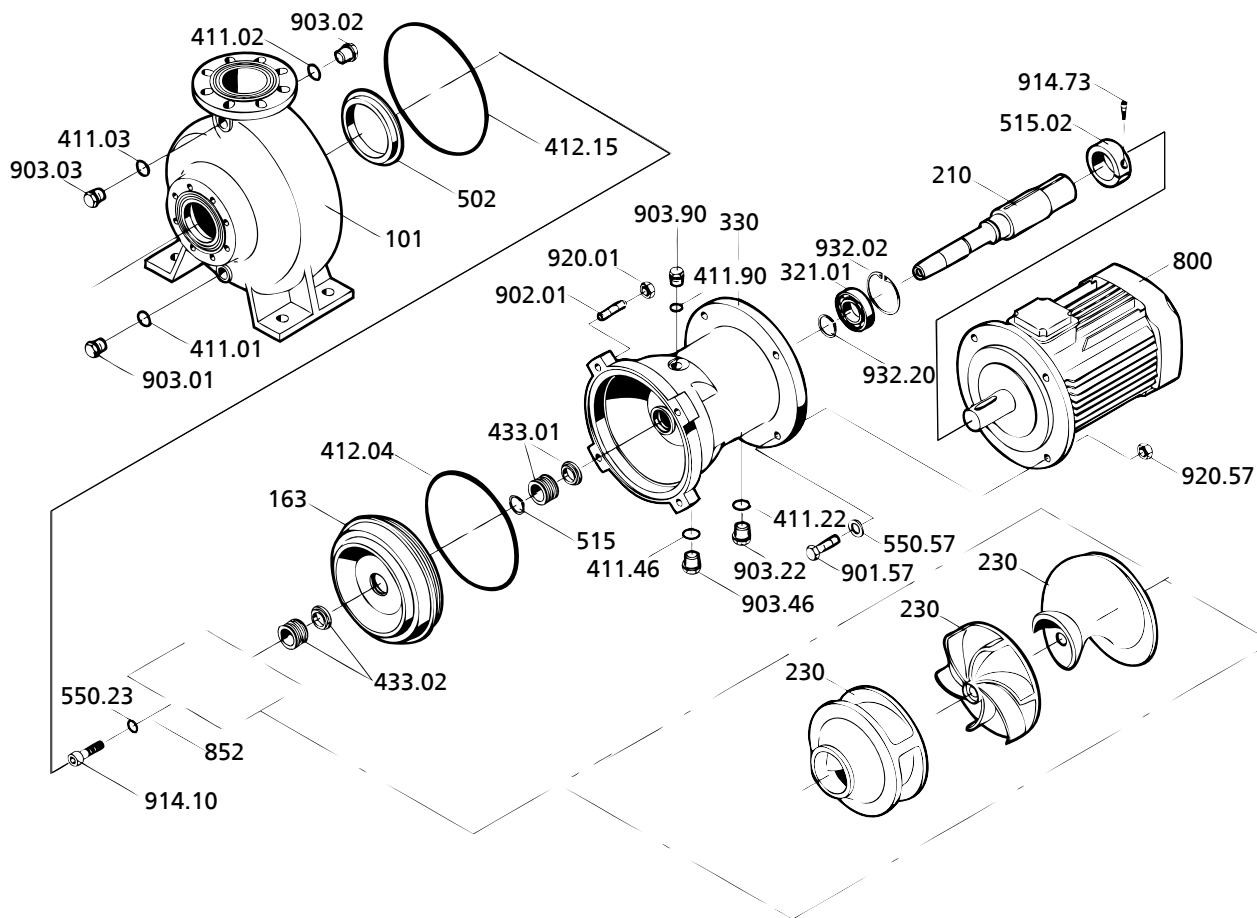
Покомпонентный сборочный чертеж Sewabloc
